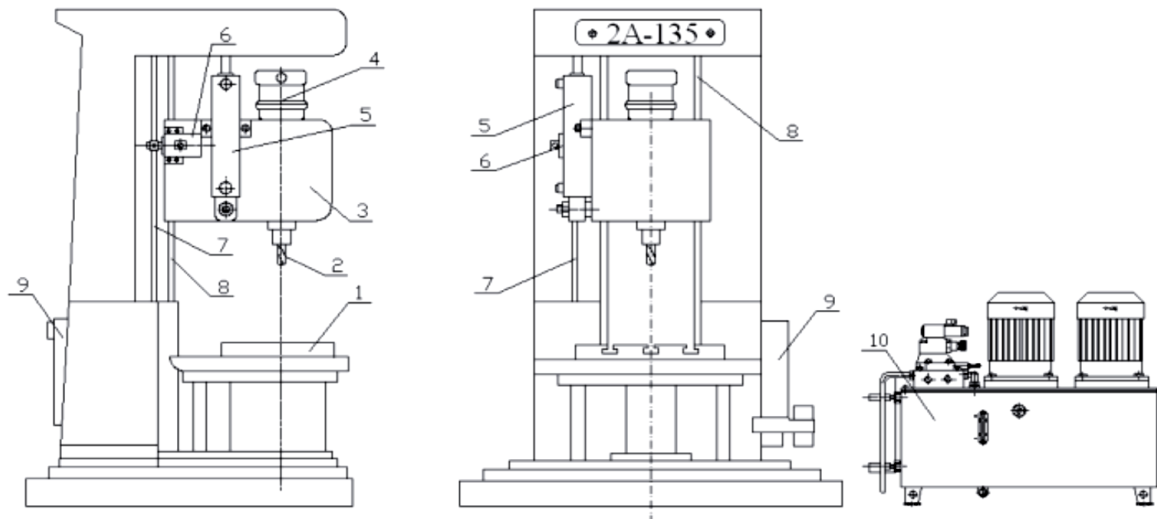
Загальний вигляд координато-свердлильного верстата 2А-135:
